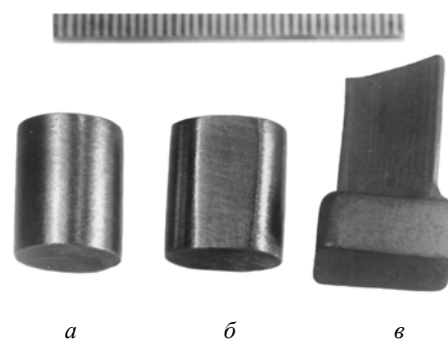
Технологические переходы при горячем выдавливании заготовки рабочей лопатки компрессора:
